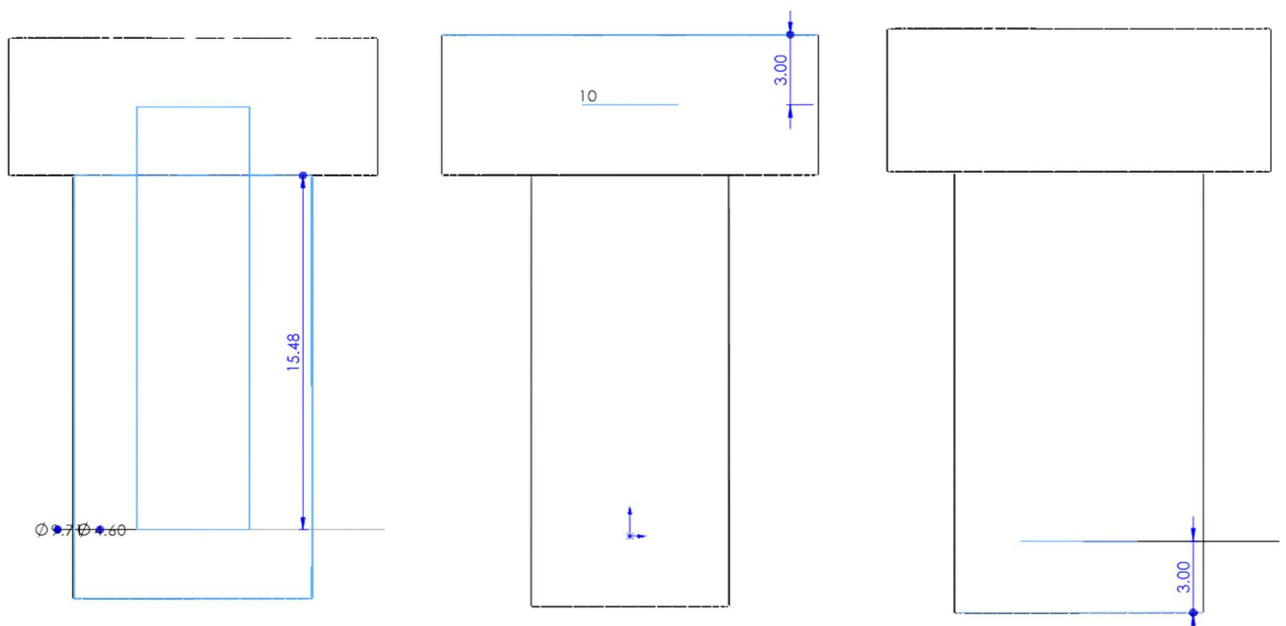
Dimensiones internas, de la tapa superior e inferior (de izquierda a derecha)
